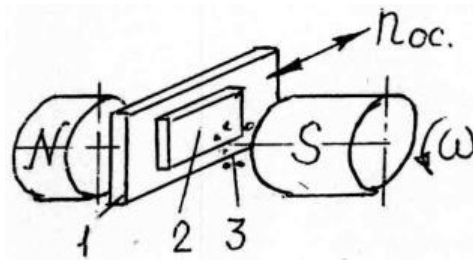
Схема округлення крайок: 1 – пластина; 2 – заготовка; 3 – феромагнітний абразивний порошок
